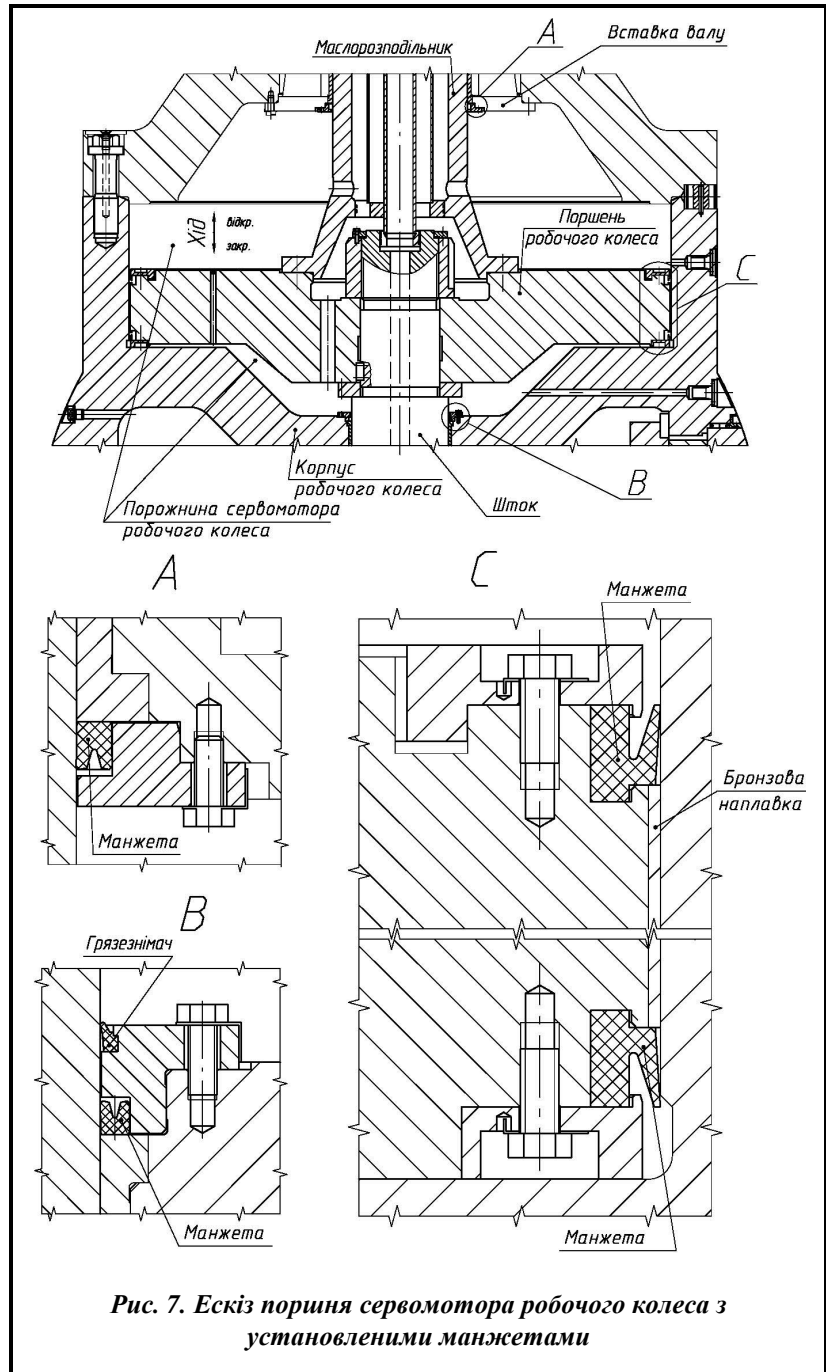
Ескіз поршня сервомотора робочого колеса з установленими манжетами
